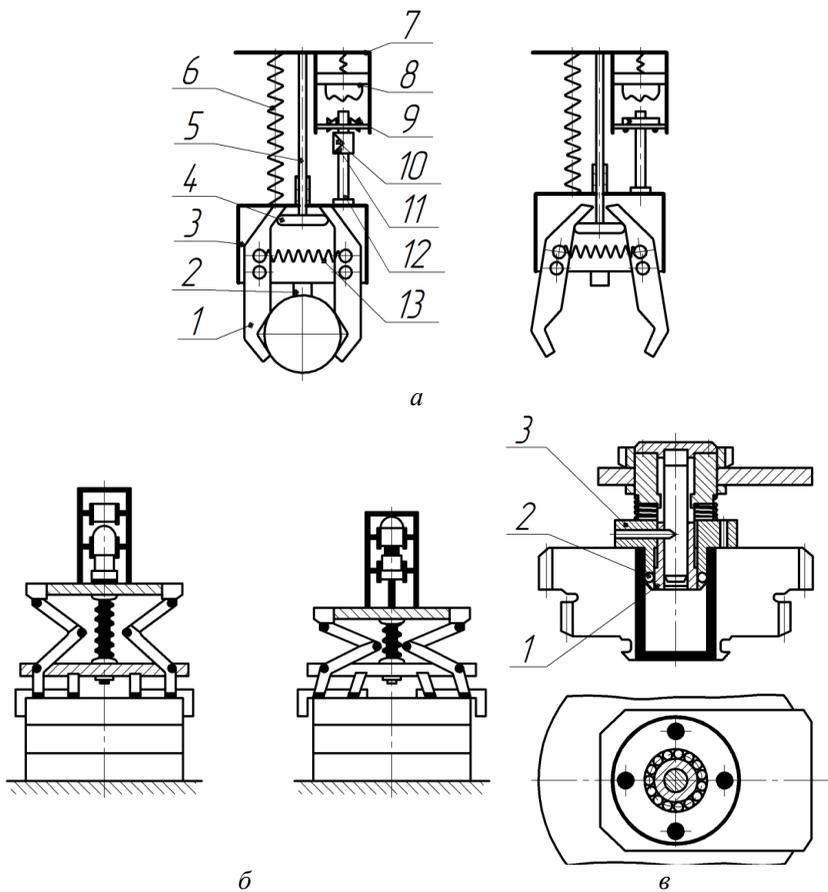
Неприводные механические захватные устройства со стопорными механизмами: *а* – ЗУ для схватывания горизонтально расположенных валов или фланцев за наружную поверхность; *б* – тактовое пружинное ЗУ для захватывания фланцев, втулок и других деталей из стопы; *в* – ЗУ для захватывания тел вращения за внутреннюю поверхность
